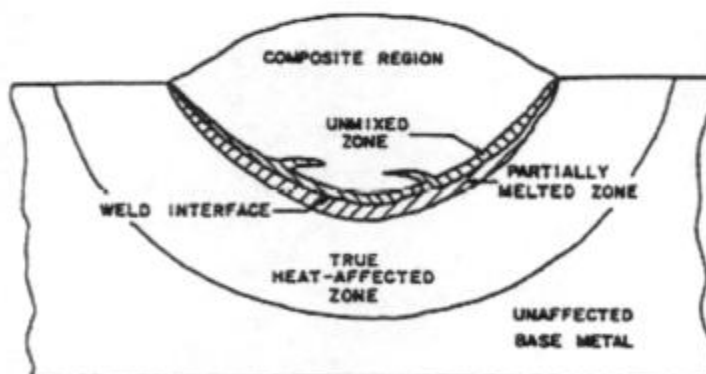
Zonas en un cordón de soldadura.(6)
